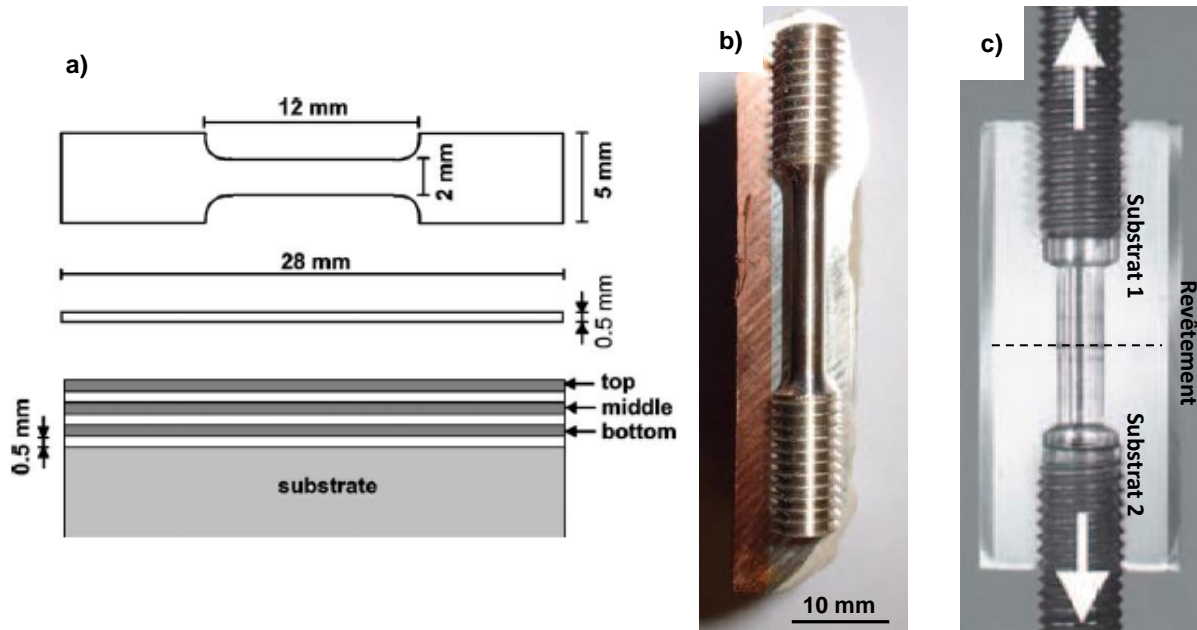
Exemple d'éprouvettes de traction cold spray : a) plate [GAR06], b) cylindrique [ROL10] et c) tubulaire [SCH06].
